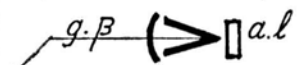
UNIONES EN ANGULO CON SOLDADURAS QUE SE CRUZAN
